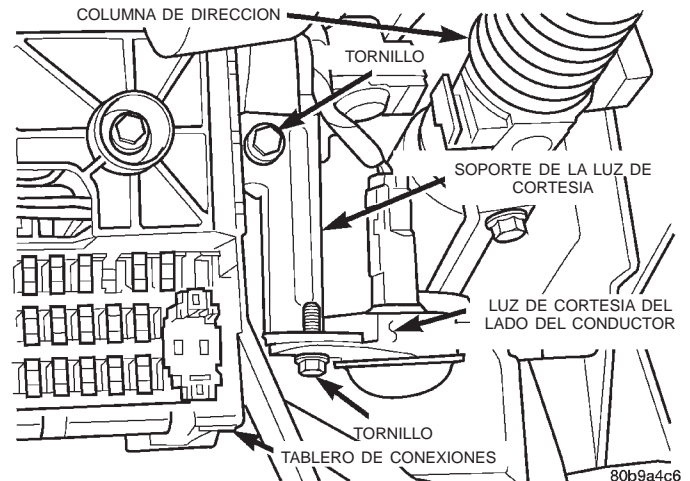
Desmontaje e instalación del soporte de la luz de cortesía del tablero de instrumentos del lado del conductor
